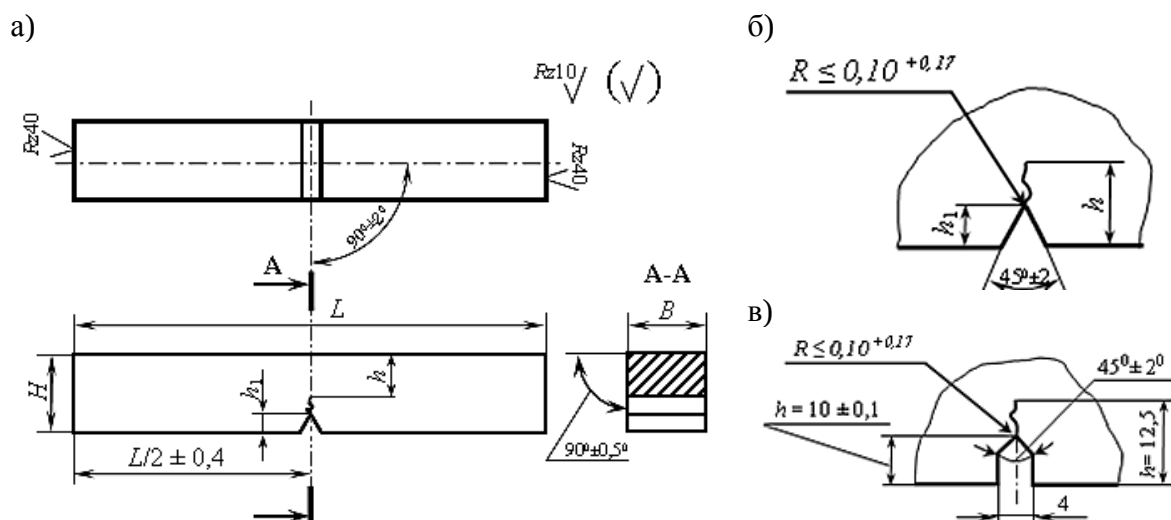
Образец с концентратором вида Т (усталостная трещина): а – общий вид; б – форма концентратора для образцов с 15-го по 19-й тип; в – форма концентратора для образцов 20-го типа
